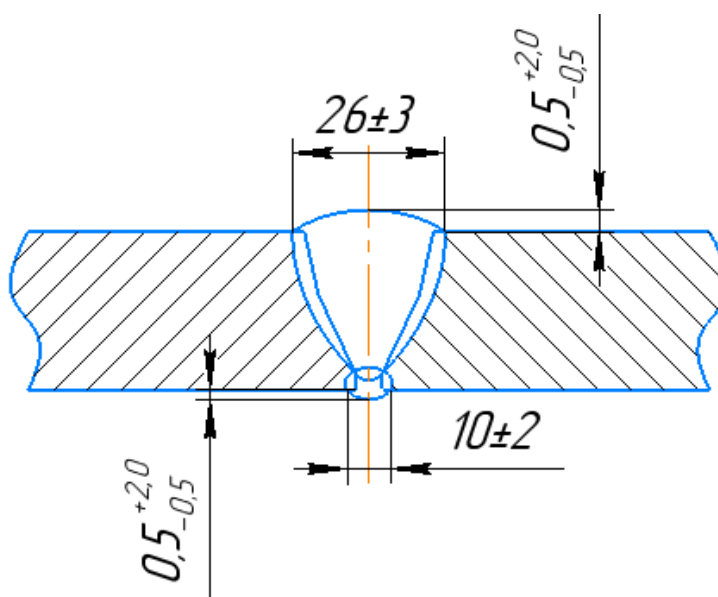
Геометрические размеры сварного шва, тип сварного соединения С24 по ГОСТ 5264-80
